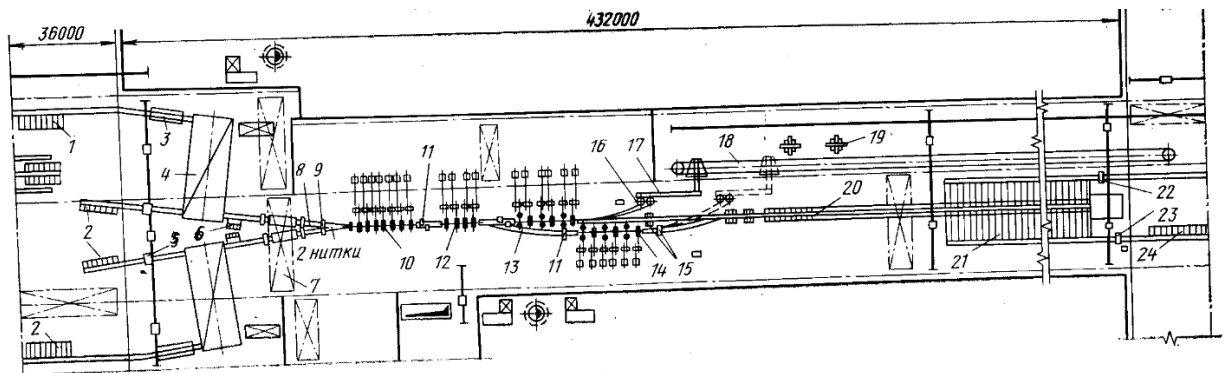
Напівнеперервний крупносортовий стан 600
